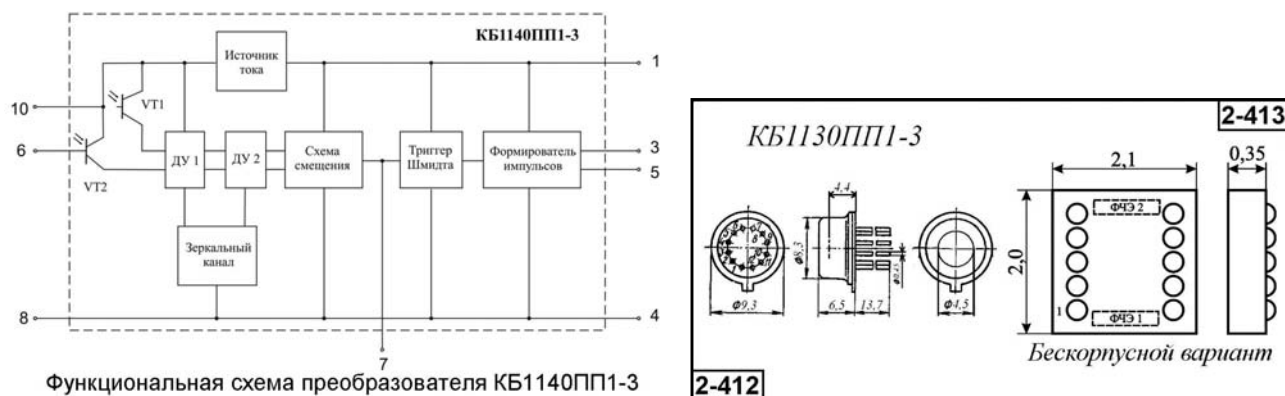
Внешний вид и габаритные размеры ФПУ КБ1130ПП1-3
